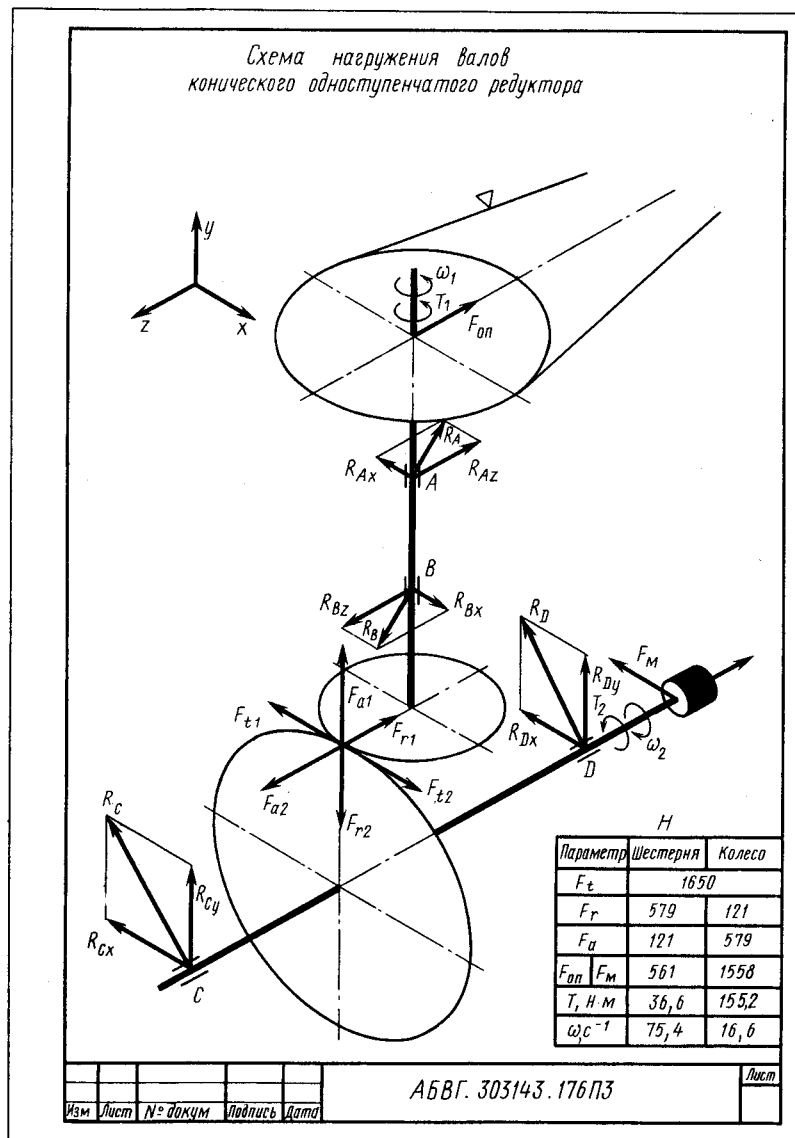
Пример схемы нагружения валов конического одноступенчатого редуктора
